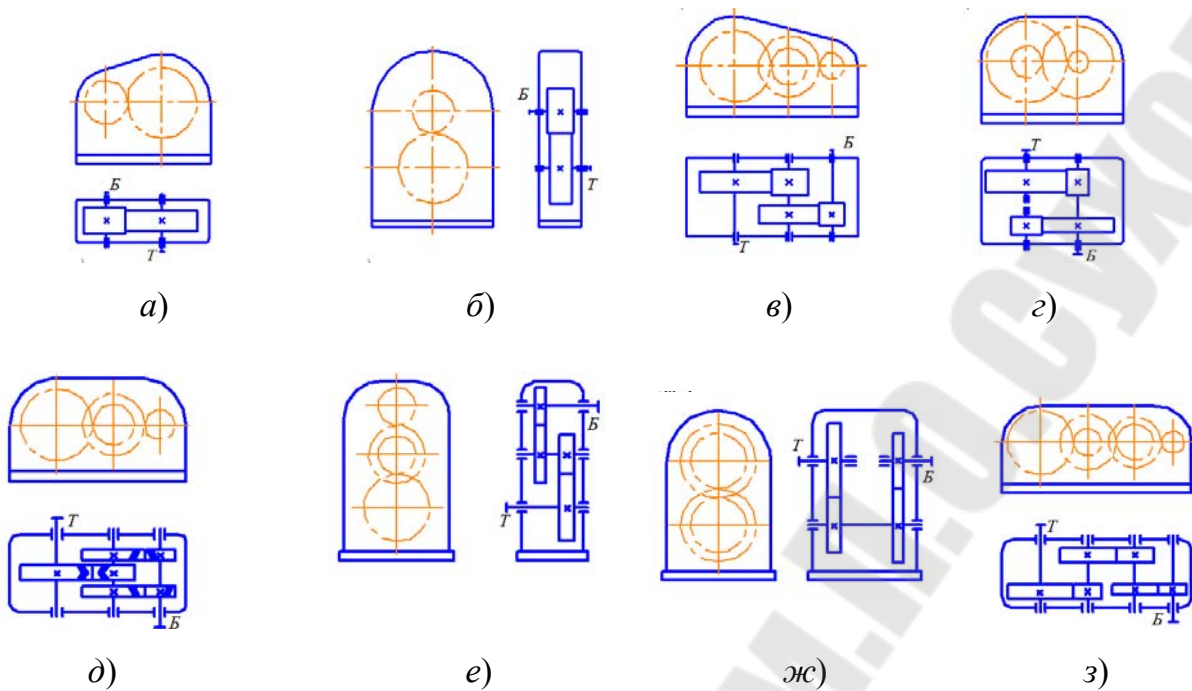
Кинематические схемы цилиндрических редукторов:
